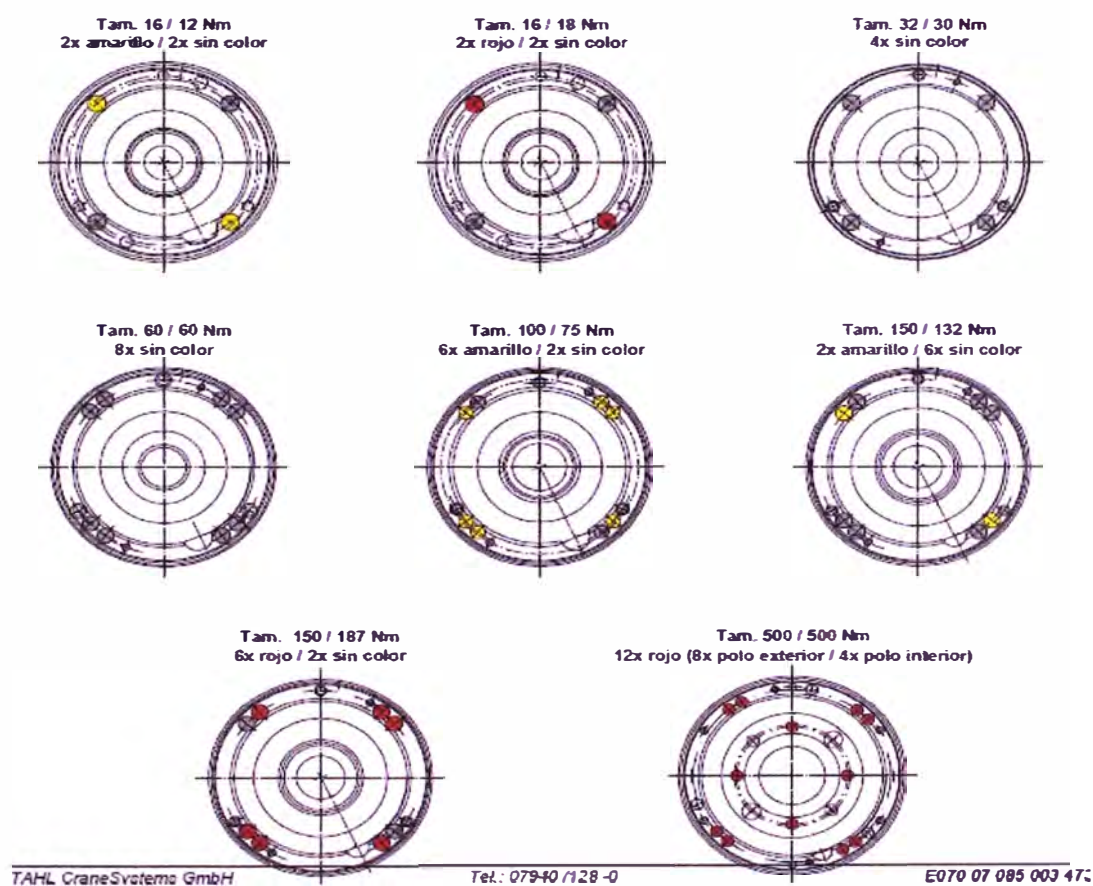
Dimensiones estándares de frenos electromagnéticos
